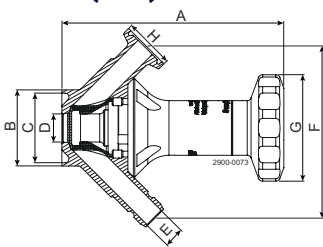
Handoberteil mit Ventilgehäuse: Rohr mit Kragen Schweißen
